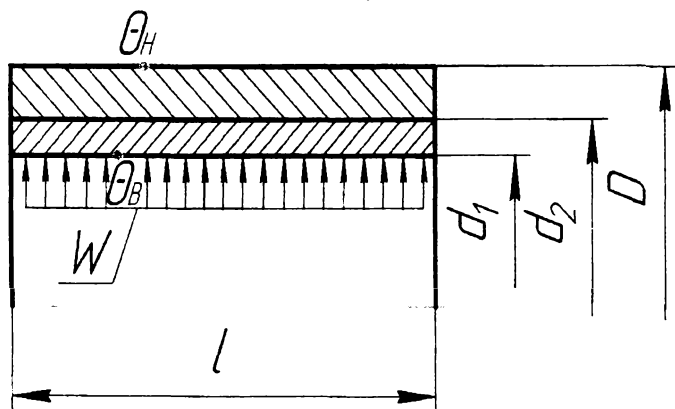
Эскиз биметаллической втулки с указанием основных размеров
